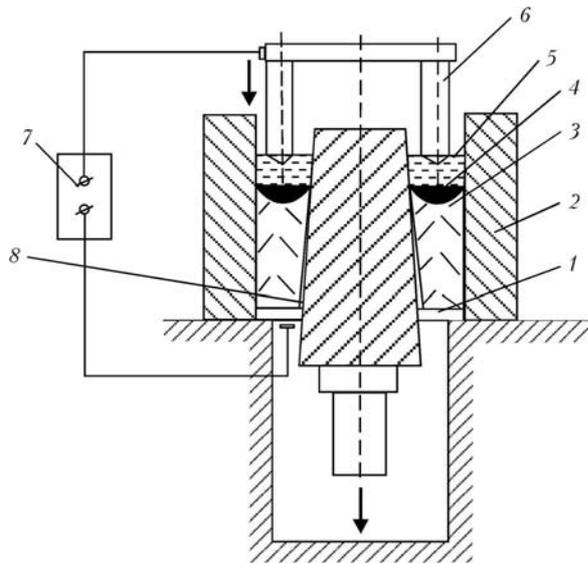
Схема ЭШЛ полой заготовки с перемещением конического дорна вниз: 8 — подвижный конический дорн
